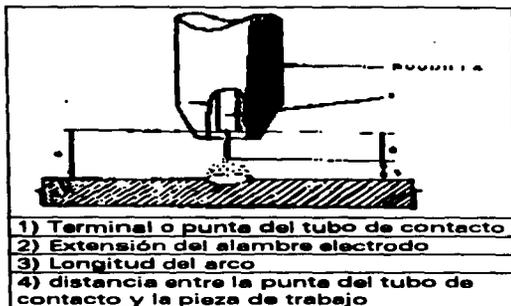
EXTENSIÓN DEL ALAMBRE ELECTRODO.
